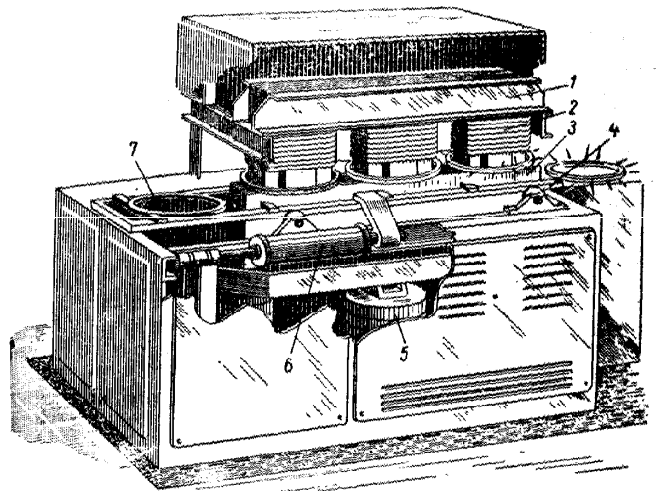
Установка для нагрева под калибровку венцов маховика автомобильного двигателя:
